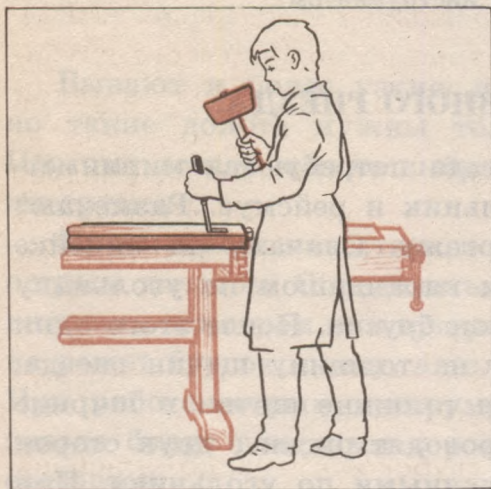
Крепление деталей в зажимах верстака при долблении.
